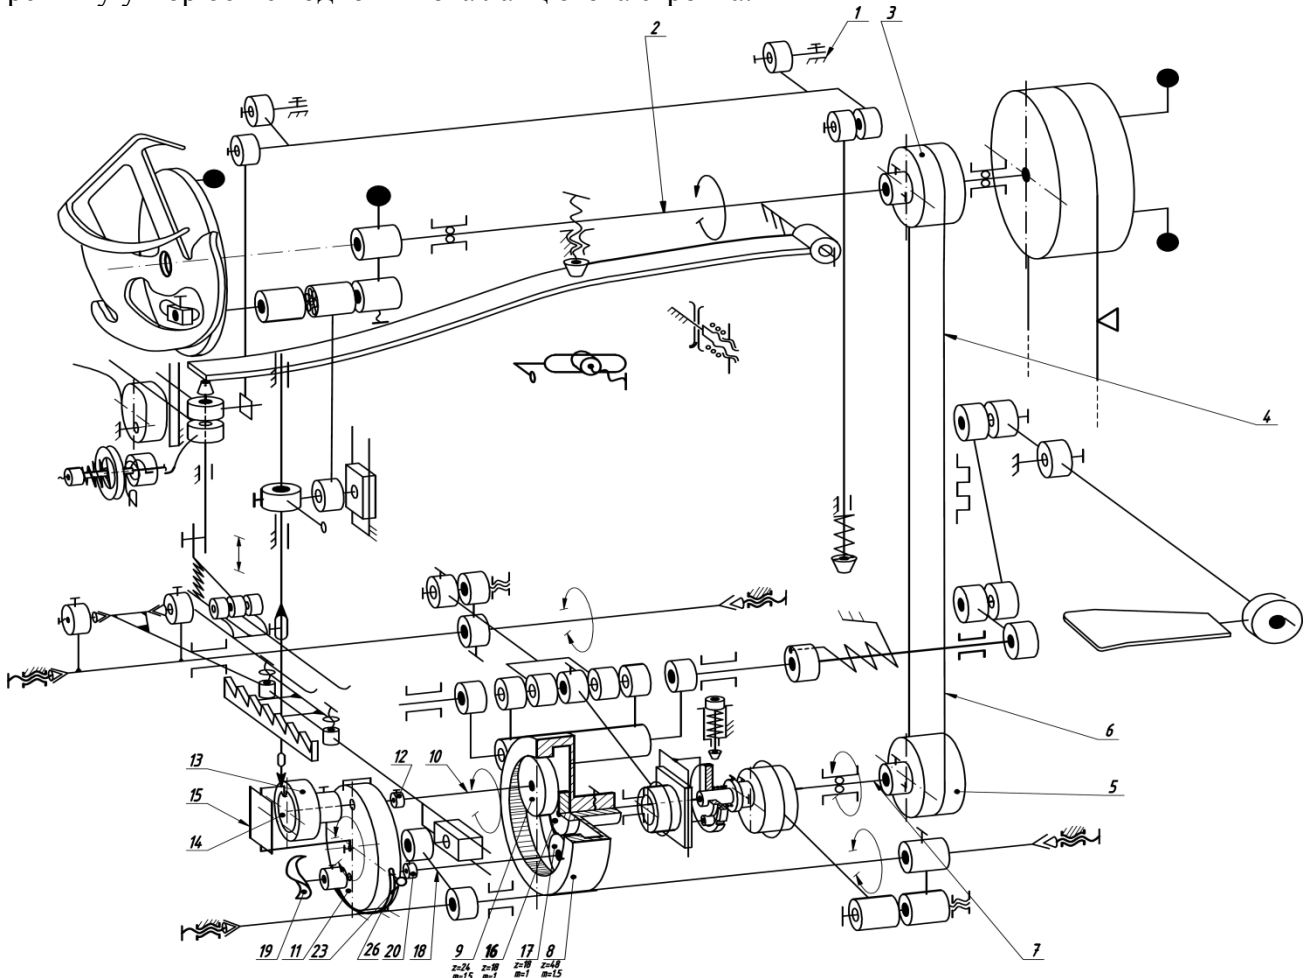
Кінематично-принципова схема петлетворних механізмів
